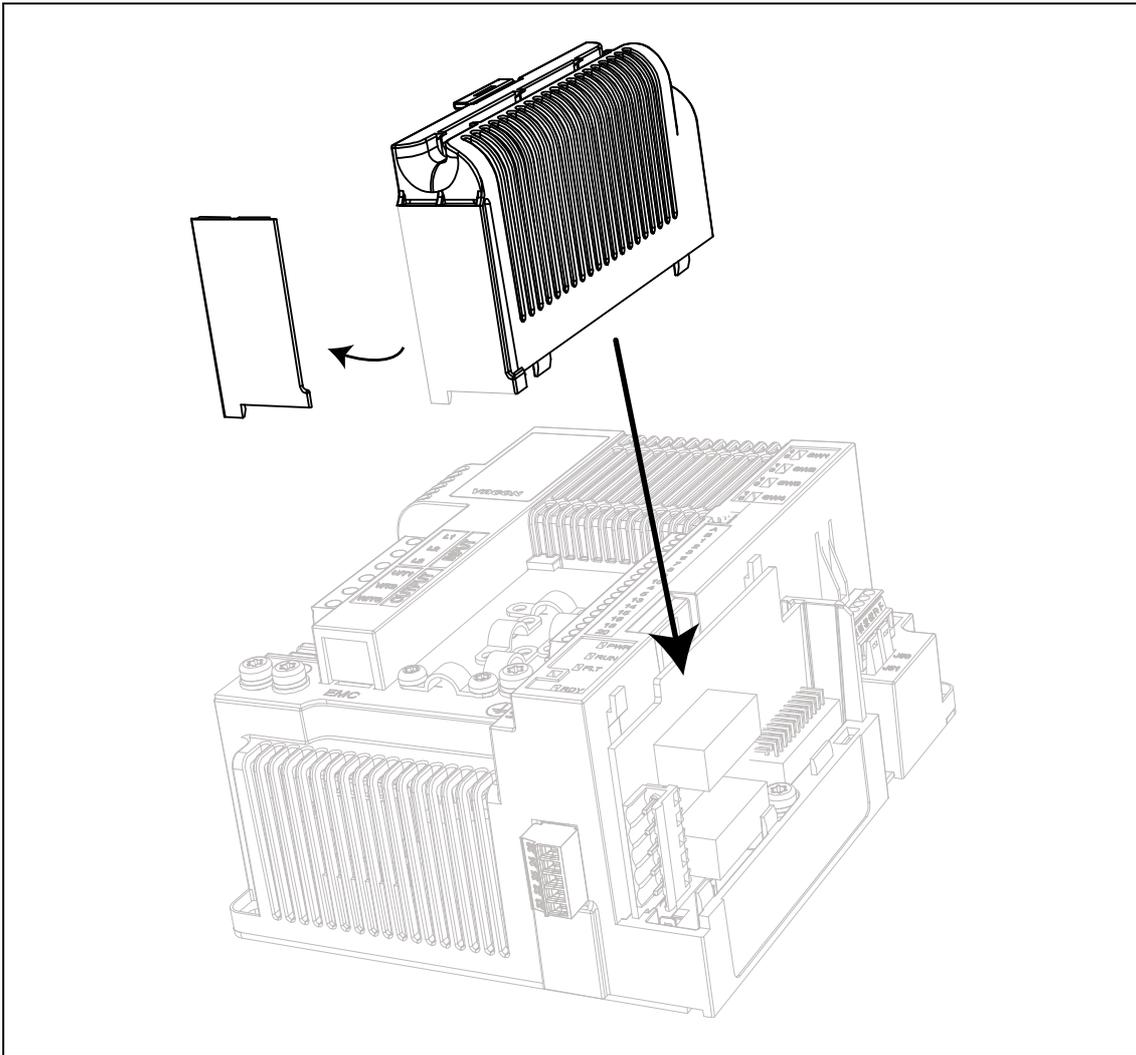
Montaje de la tapa de la ranura opcional: retirar la tapa de plástico para los bornes de la tarjeta opcional.
